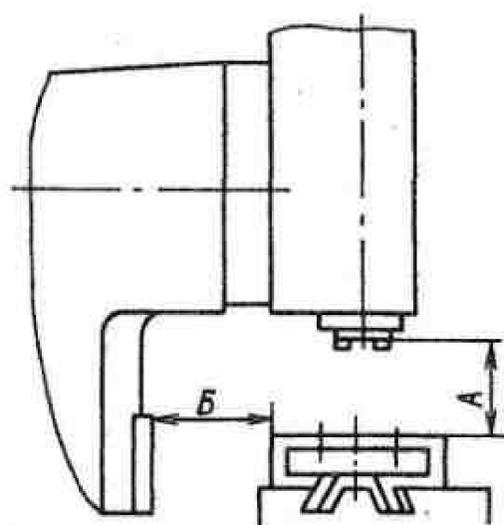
Посадочные и присоединительные размеры направляющих станины (в скобках размеры для станка 6Т13-1)
